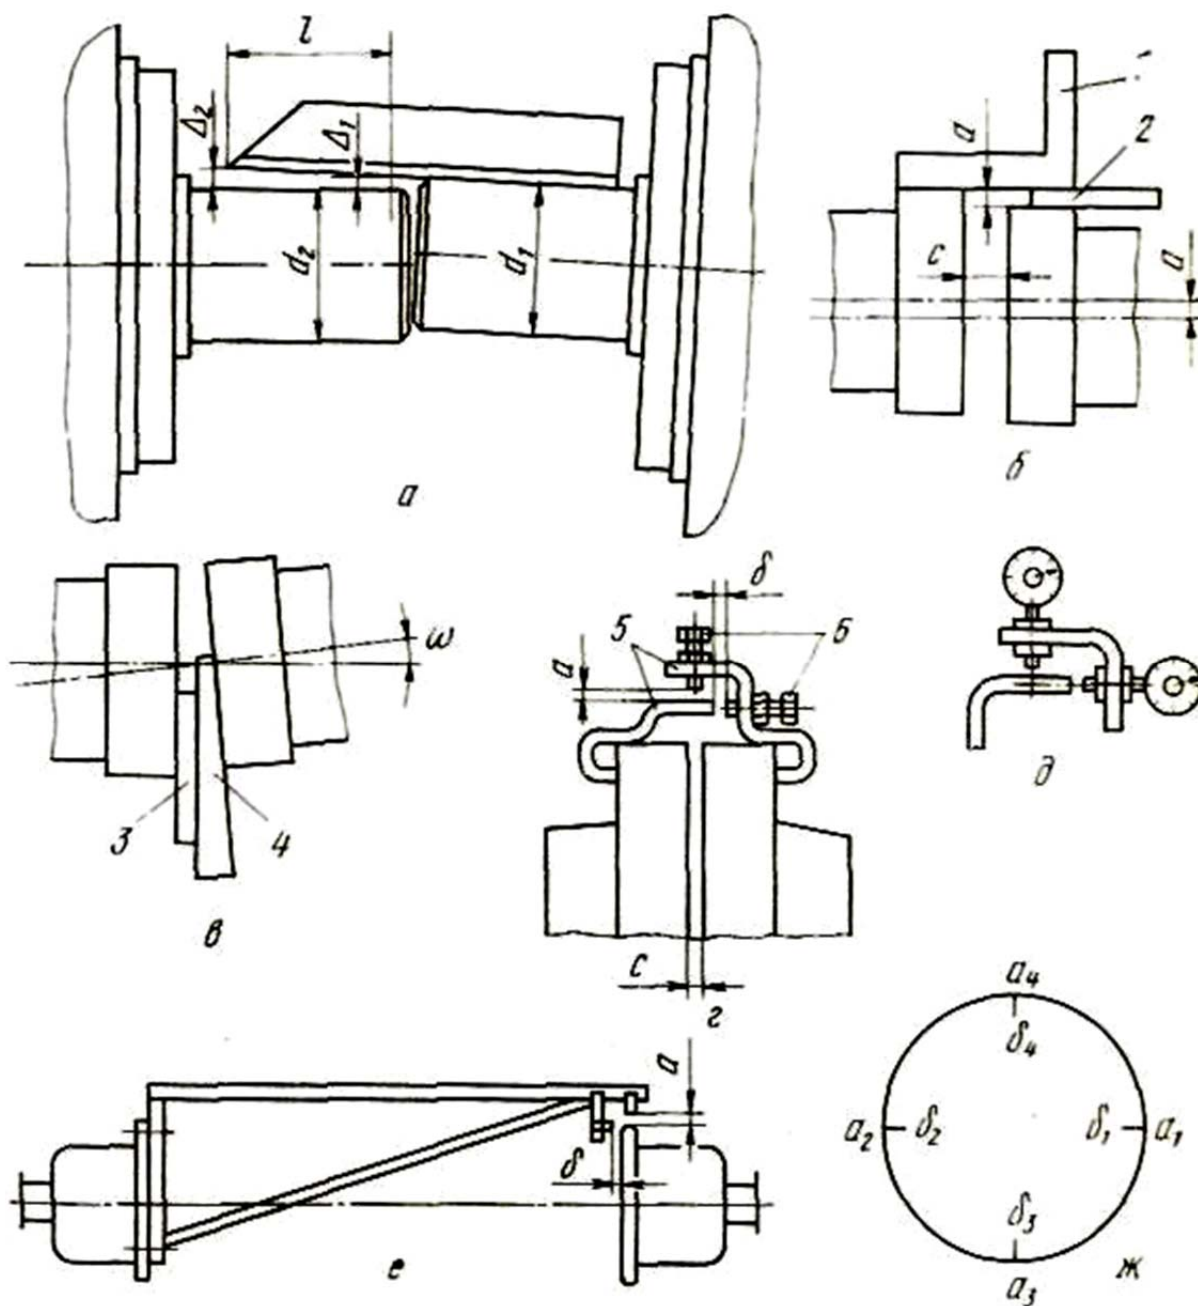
Вивіряння корпусів та центрування валів
